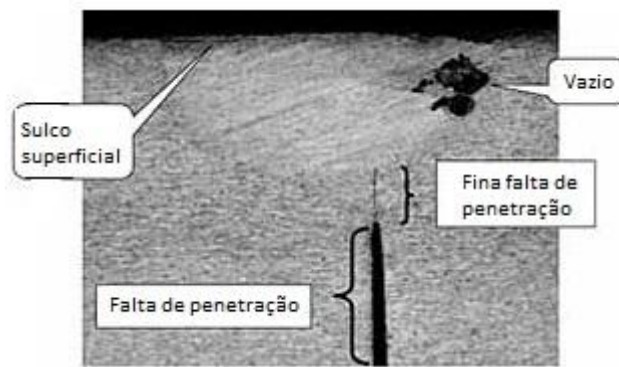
Exemplos de alguns defeitos de soldadura FSW
